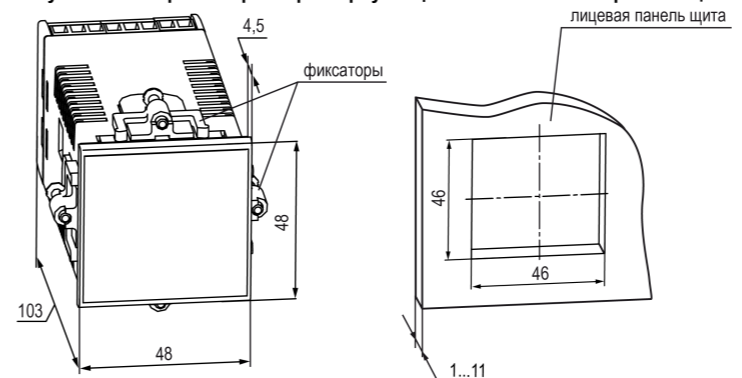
Габаритные размеры корпуса Щ5 и монтажного отверстия в щите
